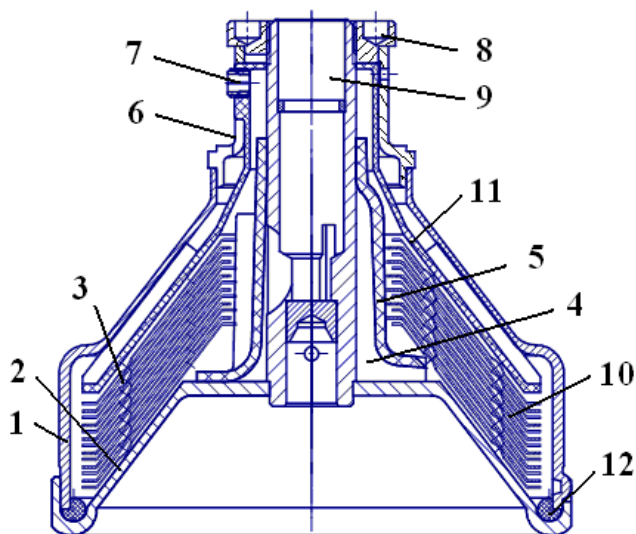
Барабан бытового сепаратора-сливкоотделителя в разрезе:
